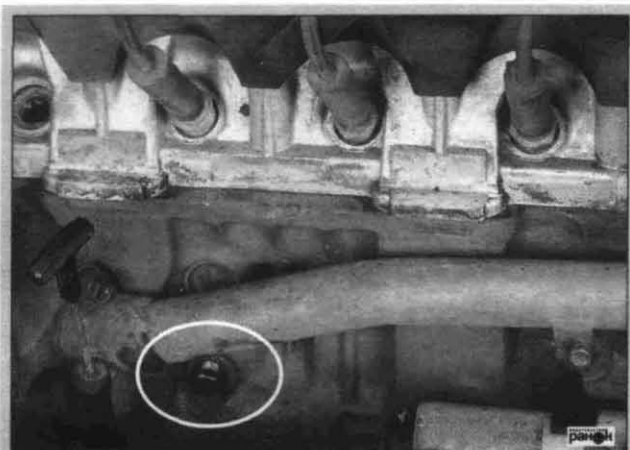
Сливная пробка охлаждающей жидкости блока цилиндров двигателя
